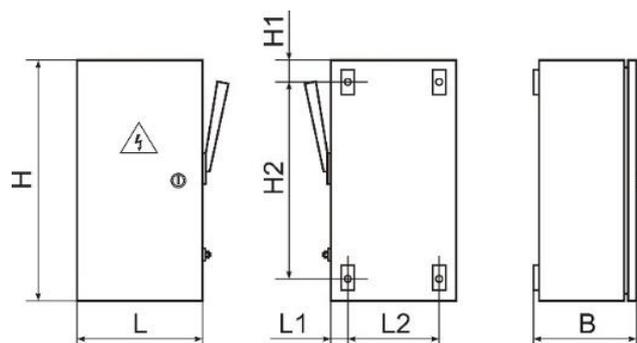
Общий вид и габаритные размеры ящиков силовых
